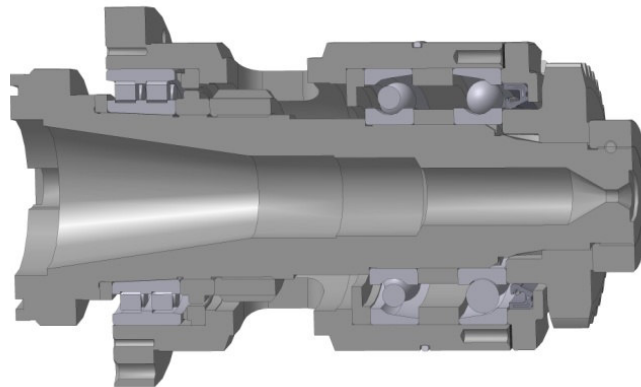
3D-модель шпиндельного узла станка СФ16МФ3
